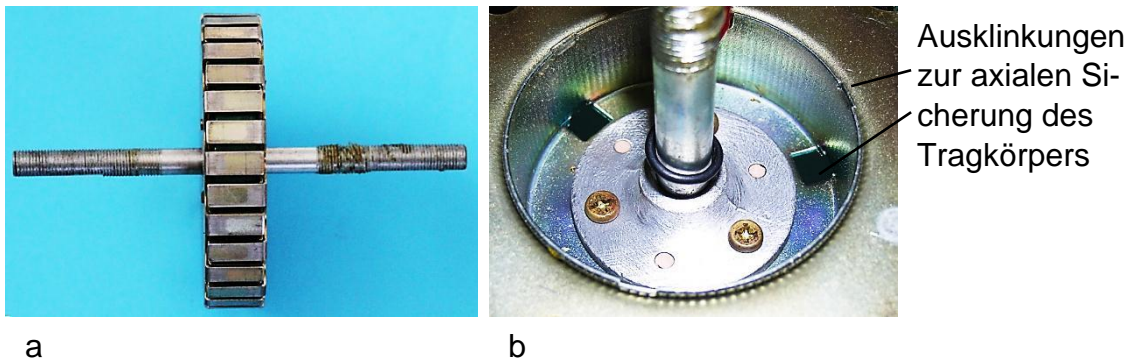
Polflächen des Klauenpolankers: a) Seitenansicht, Polschuhlänge 18 mm, Polbreite 7 mm, b) Wellenflansch mit drei Schrauben am Tragkörper befestigt.
